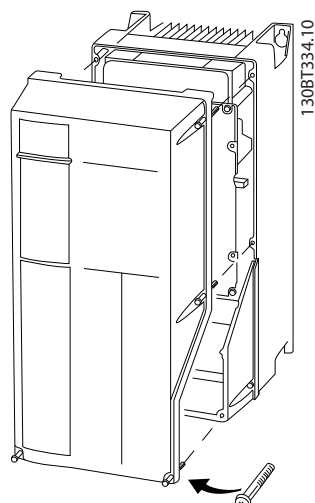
Acceso al cableado de control de las protecciones A4, A5, B1, B2, C1 y C2
